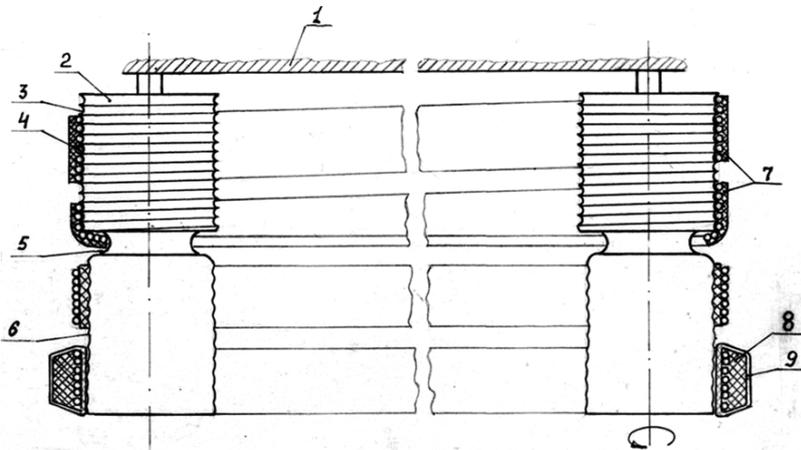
Устройства для изготовления заготовок приводных ремней (вариант 1)
